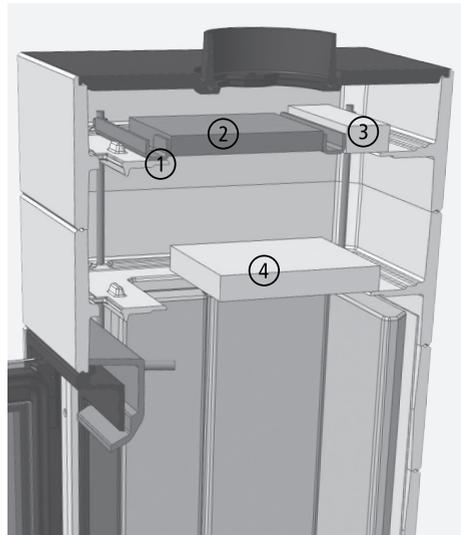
Position des plaques catalytique dans le CORNA tec, vue en coupe
